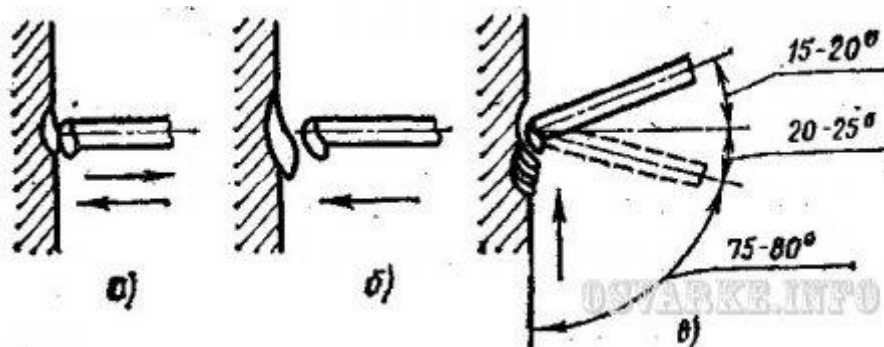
Схема техники выполнения наплавки валиков и вертикальных швов на
